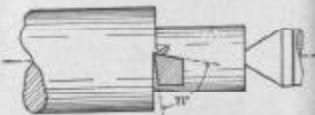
Angle d'Outil pour Tournage de la Fonte
